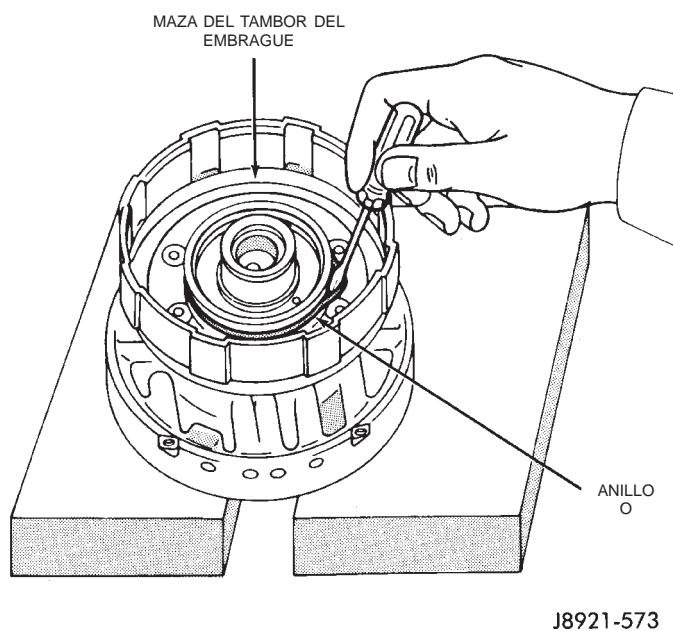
Desmontaje e instalación del anillo O del tambor del embrague
